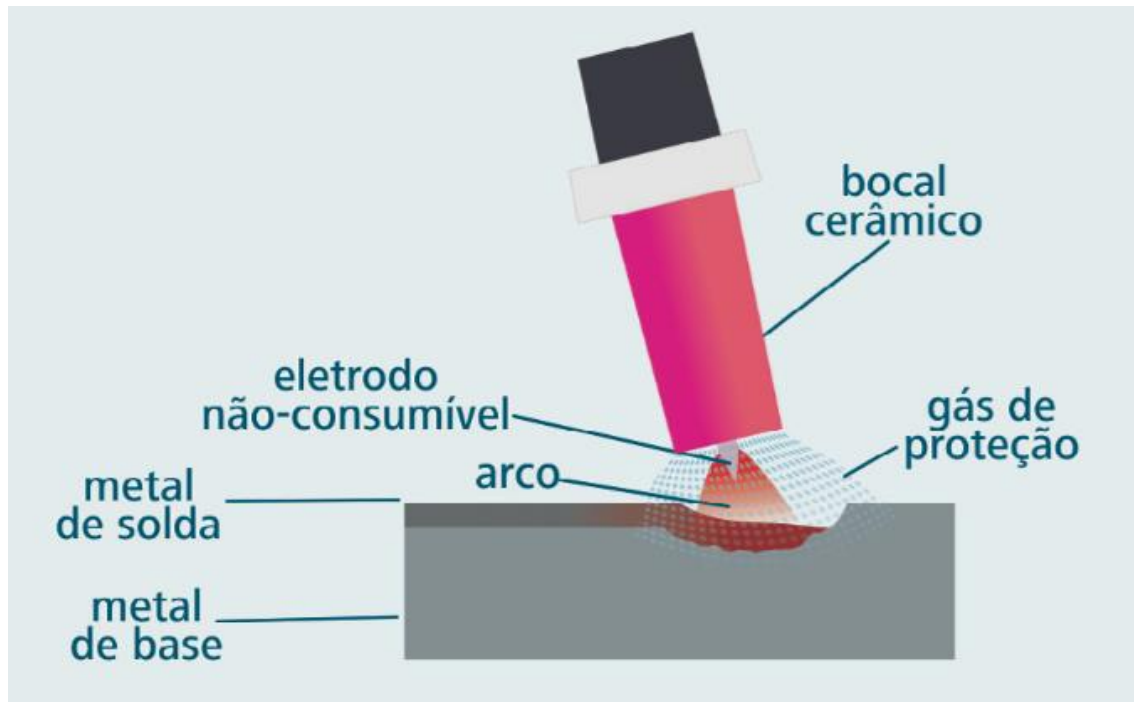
Esquema com os principais componentes do processo de soldagem TIG [45, 51].
